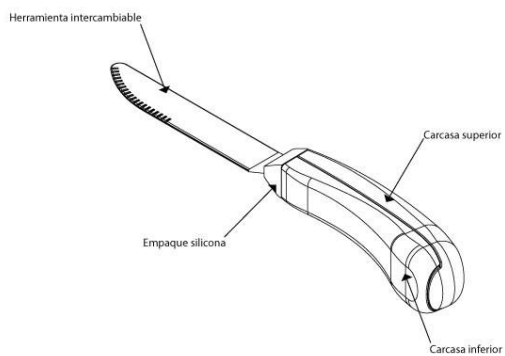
Ensamblado CUCHILLO. Fuente: Losada, J. (2014).
